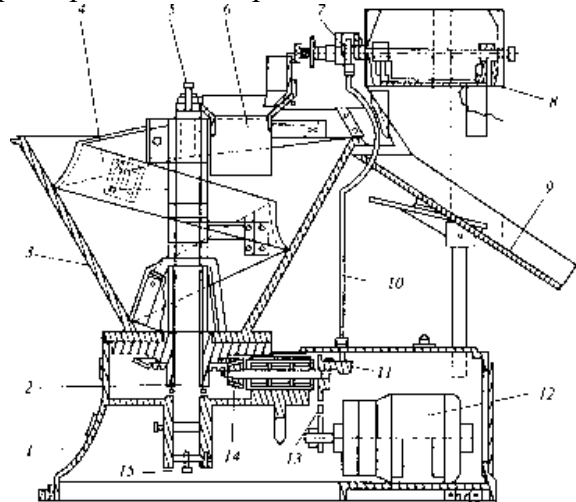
Конструктивная схема тестоокруглительной машины: 1 - станина; 2 - стойка; 3 - чаша; 4 - спиральный желоб; 5, 15 - винты; 6 - приемная воронка; 7 - кривошип; 8 - мукопосыпатель; 9 - наклонный спуск; 10 - тяга; 11 - палец звездочки; 12 - электродвигатель; 13 - цепная передача; 14 - зубчатая передача
